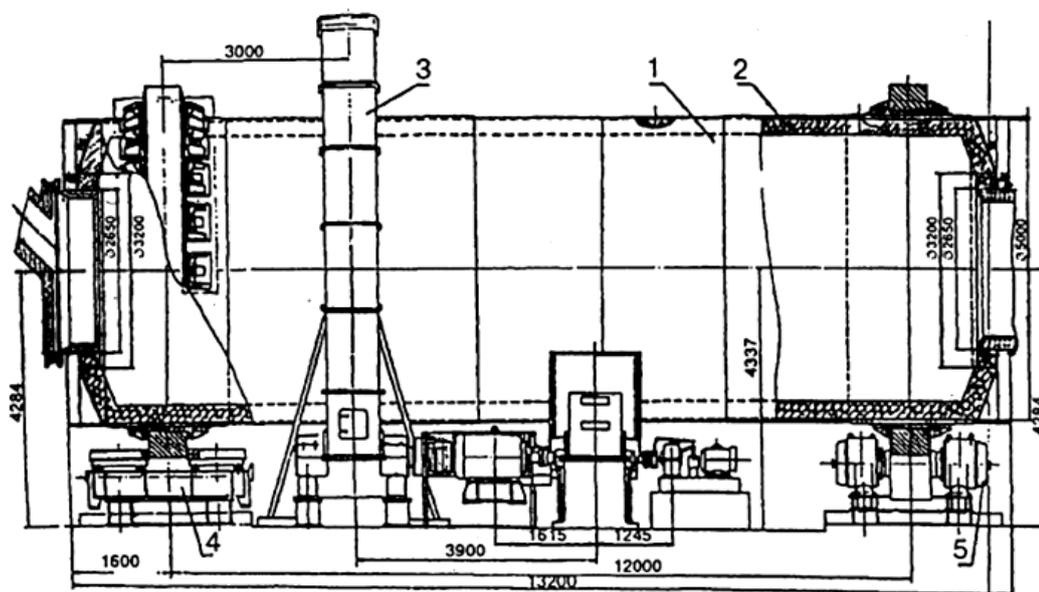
Барабанный реактор: 1- корпус реактора, 2-футеровка (обмуровка),3 привод,4-5 подшипники
